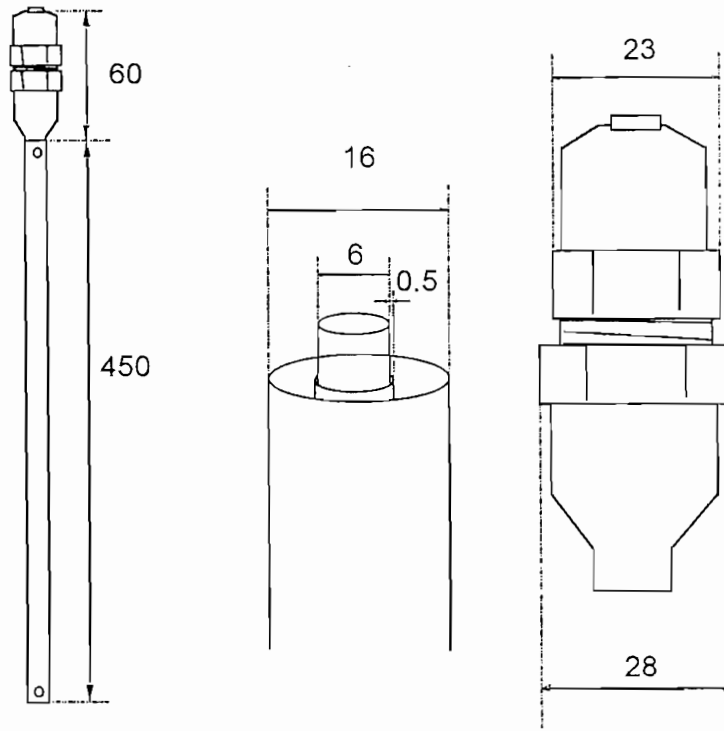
Esquema constructivo del sensor capacitivo. Medidas en milímetros.
